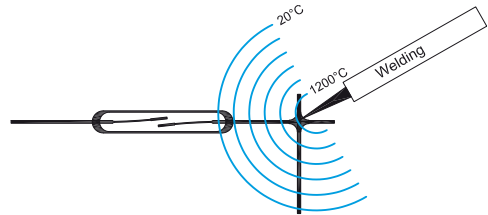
Löten und Schweißen kann einen Hitzeschock auf die Glas-Metalleinschmelzung erzeugen.
